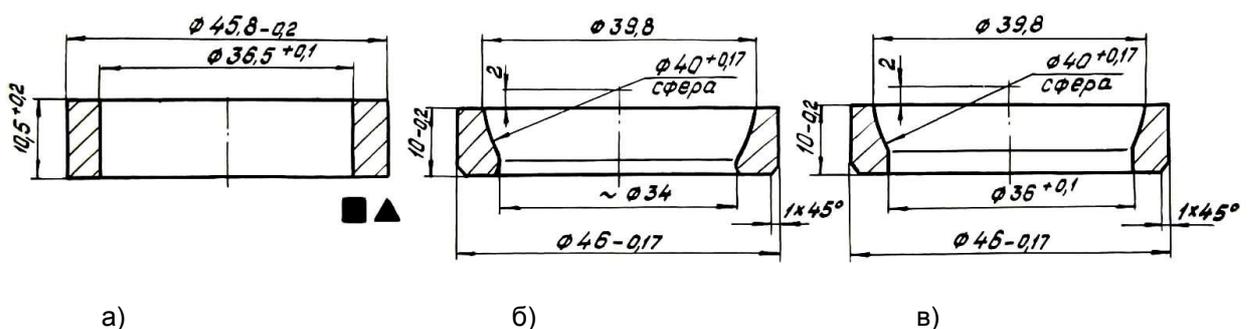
Переходы холодной объемной штамповки «сферической опоры» с деформированием трубной заготовки пуансоном без оправки
